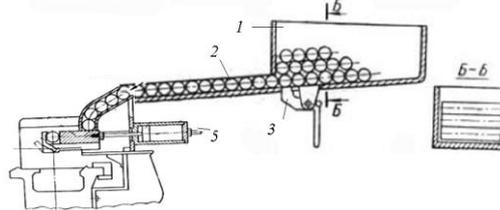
Схема бункерного магазина с возвратно-поступательным двигателем
